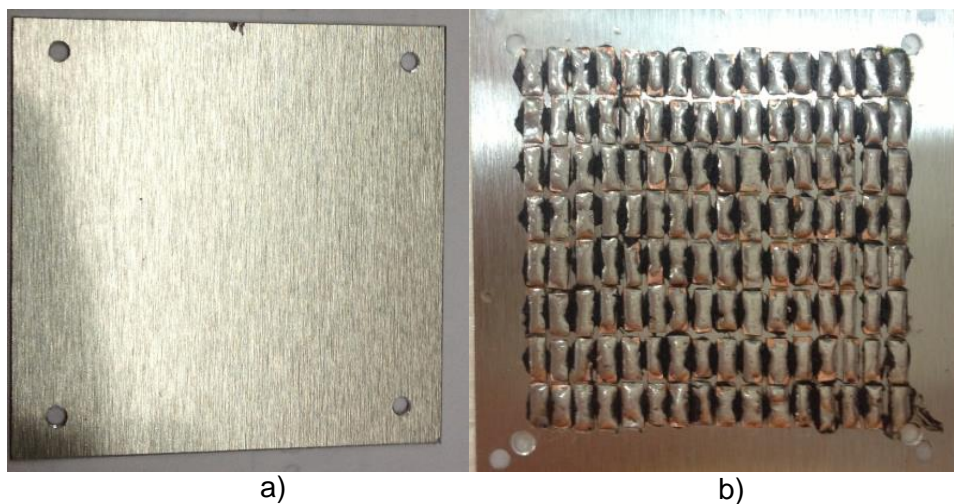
a) Placa de aluminio anodizado b) Placa con contactos de cobre y soldadura
